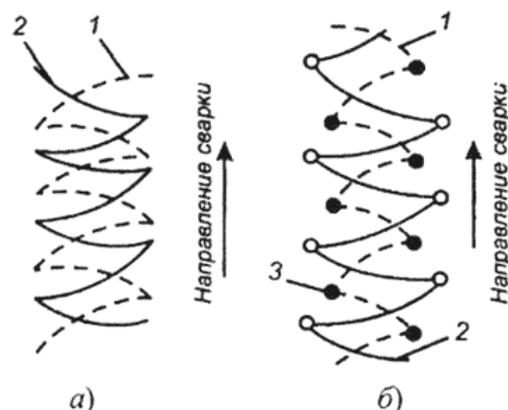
Способы перемещения горелки (способы газовой сварки)
